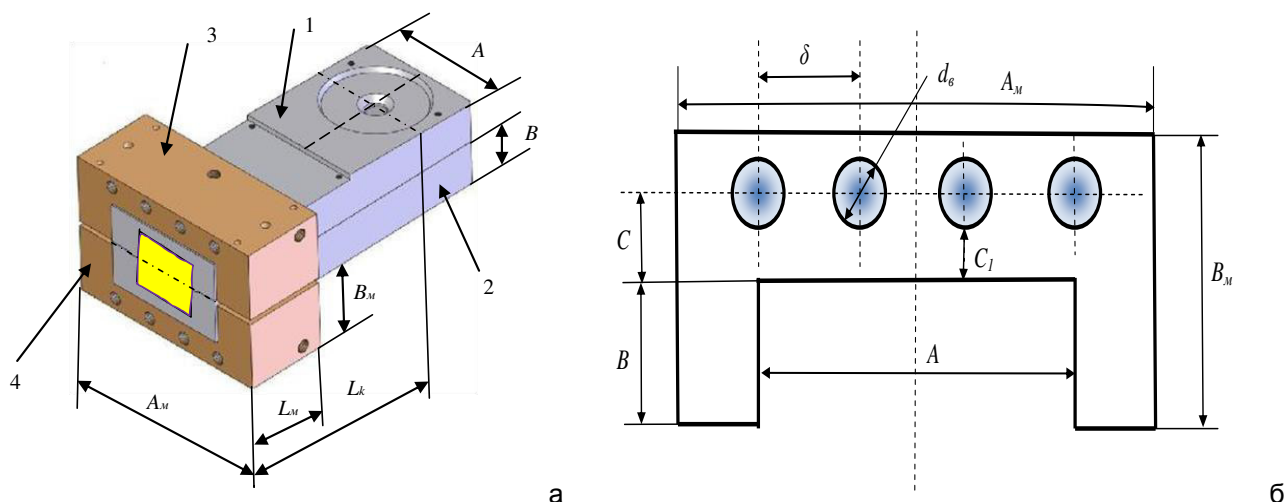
Основные размеры верхнего (1) и нижнего (2) частей графитового кристаллизатора и верхнего (3) и нижнего (4) частей медного охлаждающего устройства ГМПЛЗ для получения заготовок прямоугольного сечения (а); (б) – основные размеры медного охладителя с цилиндрическими водяными каналами
